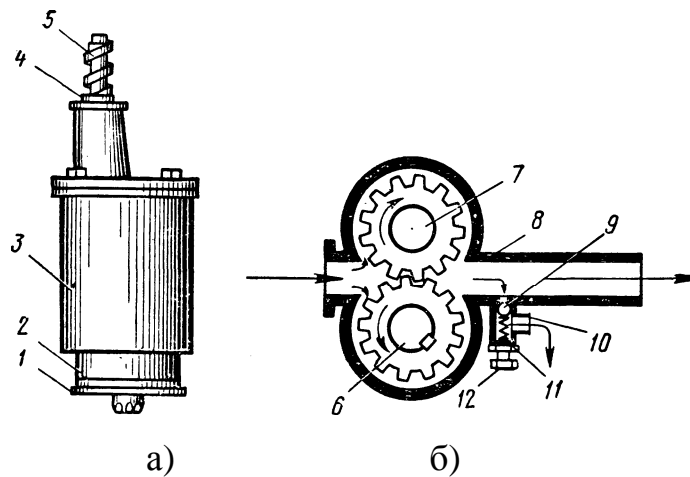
Мазильний шестеренний насос (а), схема його роботи й устрій редукційного клапана (б):
